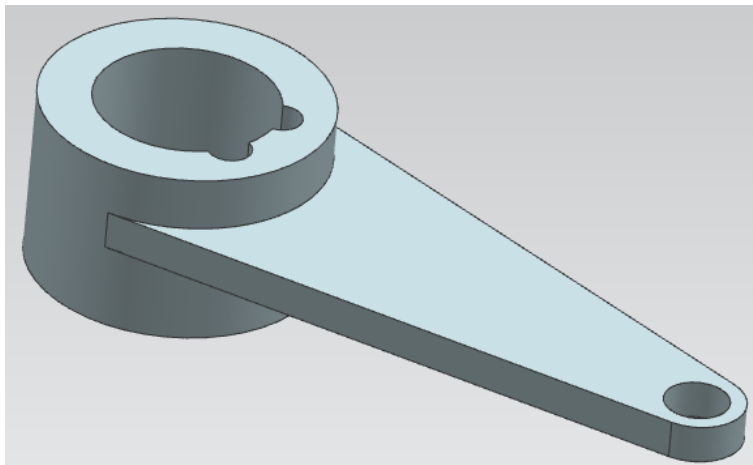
CAD Modell eines Hebels für die Ausführung mit Biegeelenker
